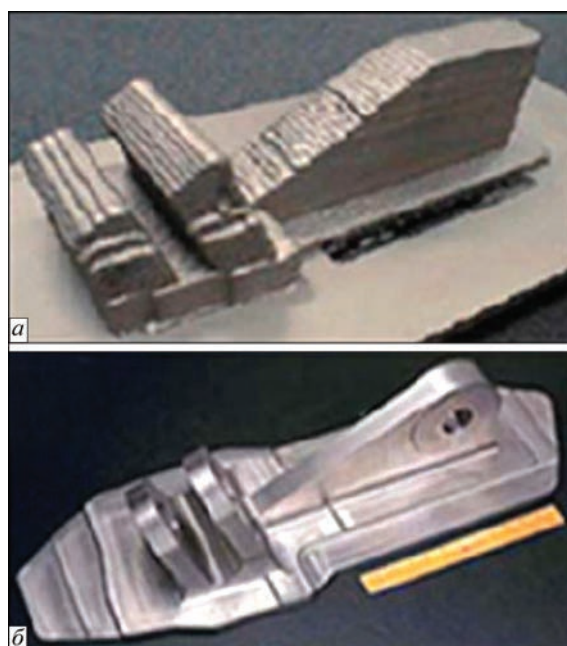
Заготовка (а) детали (б) выполненной способом WFLB
